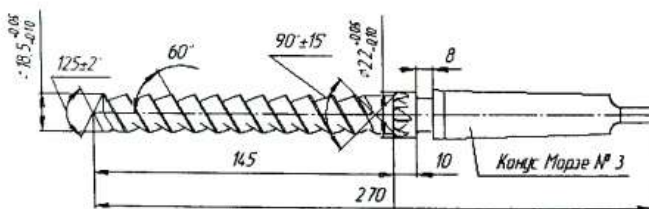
Комбінований металорізальний інструмент: свердло-зенківка
